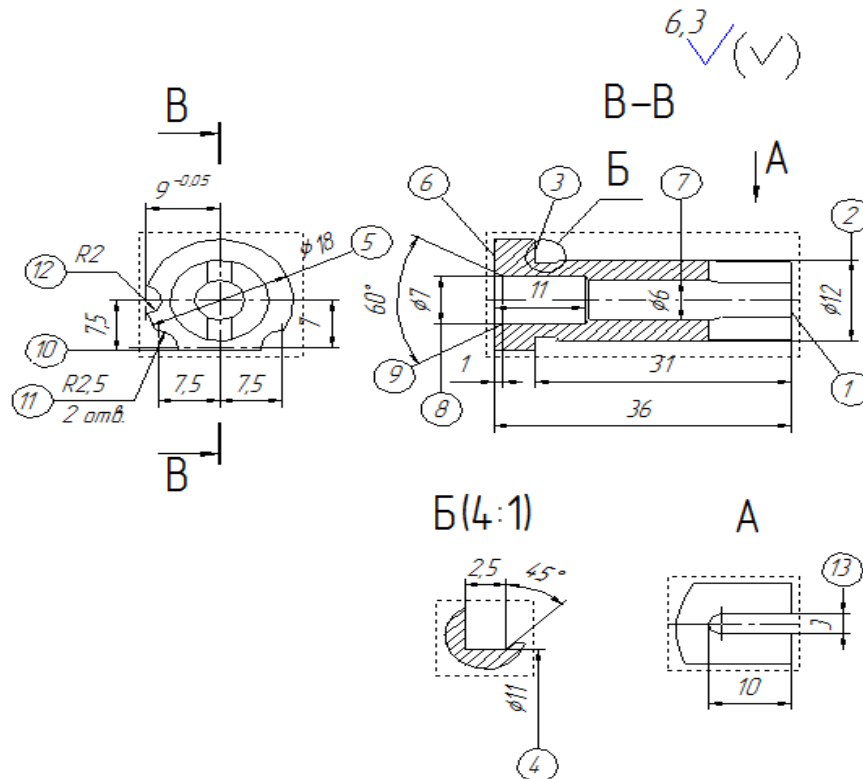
Позначення поверхонь деталі "Втулка"
